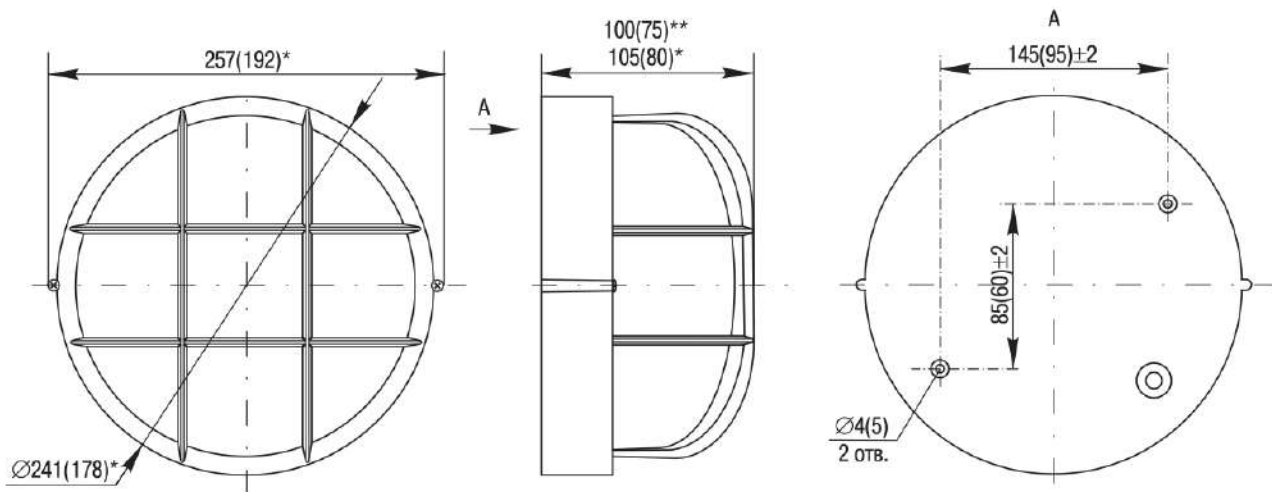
Габаритные и установочные размеры светильников НПП 1102...1108
